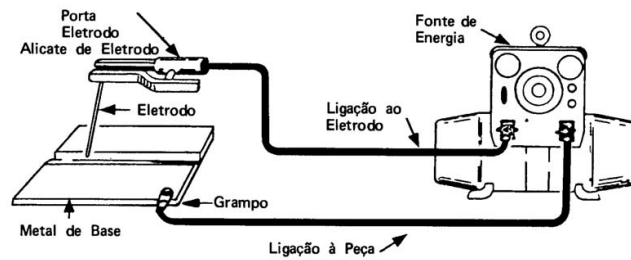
Processo de soldadura com eléctrodo revestido [16]
